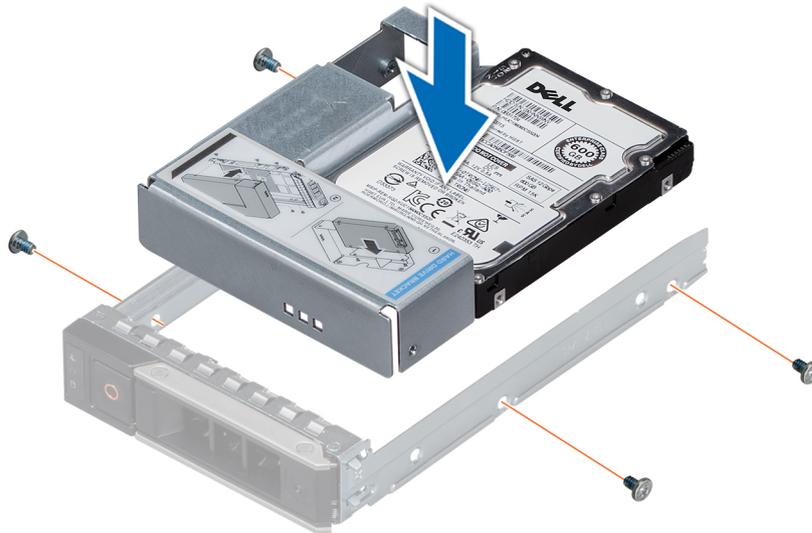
Installieren eines 3,5-Zoll-Adapters in einem 3,5-Zoll-Laufwerksträger
